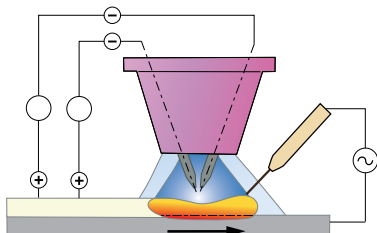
Схема сварочного процесса TIG<sup>er</sup> со сдвоенной ВИГ-дугой. Оба вольфрамовых электрода и подогреваемая присадка подсоединены к одному источнику тока, причем для подогрева присадки применяется переменный ток, чтобы избежать воздействия дуги.
